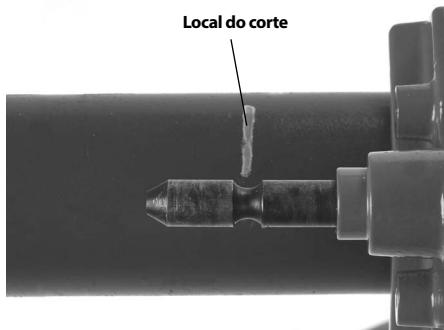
Posicionamento do dispositivo de suporte alinhado com o local de corte pretendido
